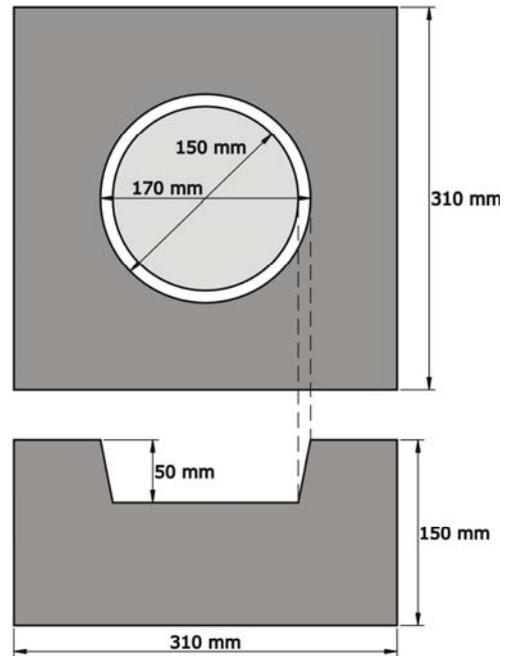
Dimensões molde utilizado para obtenção das espumas.
